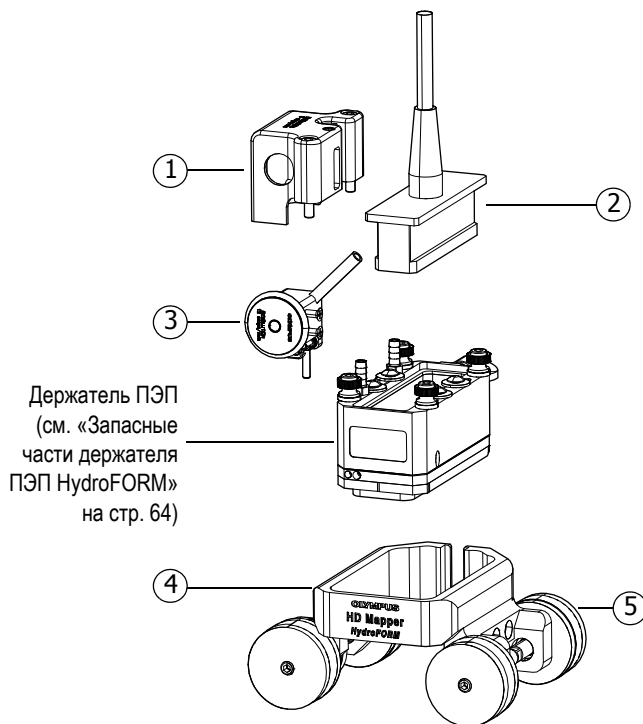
Сборочный чертеж сканера HydroFORM
